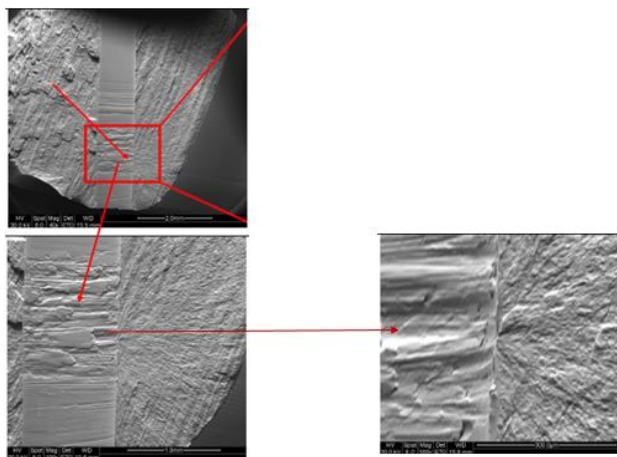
Exemplo de trinca devido a defeito de usinagem e aspecto de fratura e local do início da trinca.
